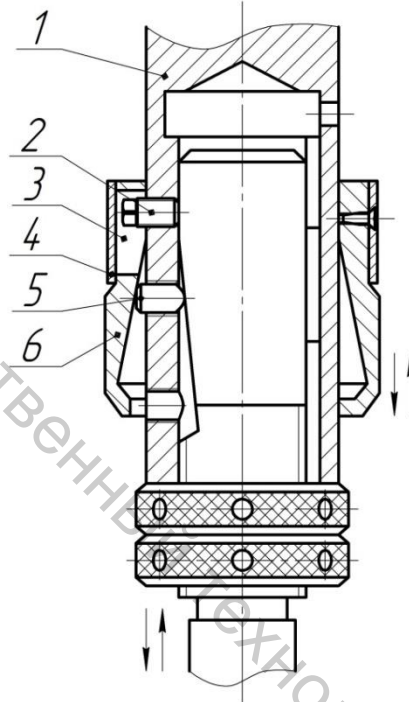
Шпиндель сверлильного станка с базами по ГОСТ 13876–87, модернизированный под схему «быстрого зажима»: 1 – шпиндель; 2 – стопорный винт; 3 – паз; 4 – кожух; 5 – плунжер; 6 – втулка зажимная
